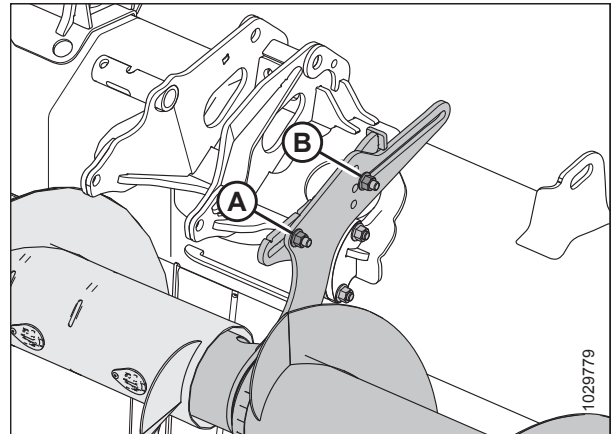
Posición inicial de los montajes ajustables: sinfín de tres piezas
